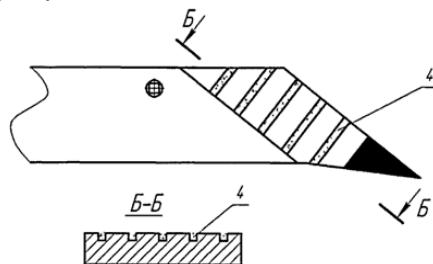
Лемех с пазами, прорезанными в носовой части и с заплавленной заглубляющей частью (1 - рабочая поверхность носка лемеха; 2 - пазы; 3 - наплавленная поверхность; 4 – почвенная масса)
